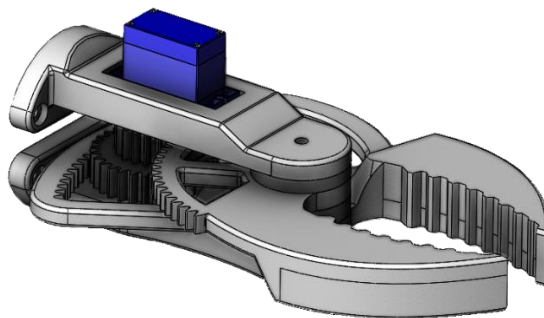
Розроблений захватний пристрій робота-маніпулятора
